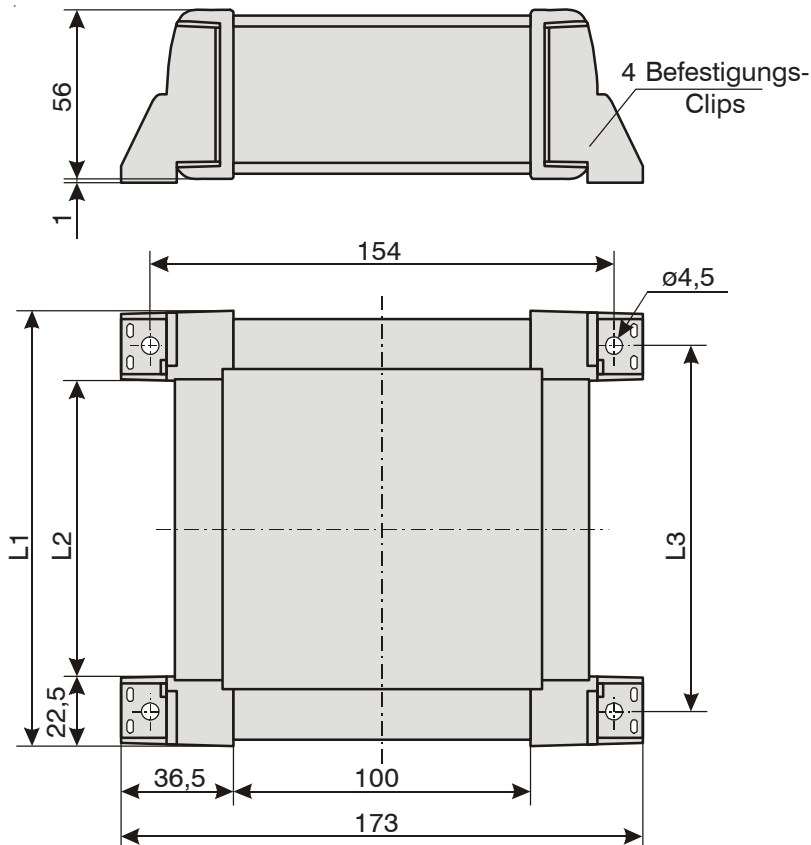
Maßzeichnung des Controllers 1800/1801 mit Montagewinkel (nicht maßstabsgetreu)
